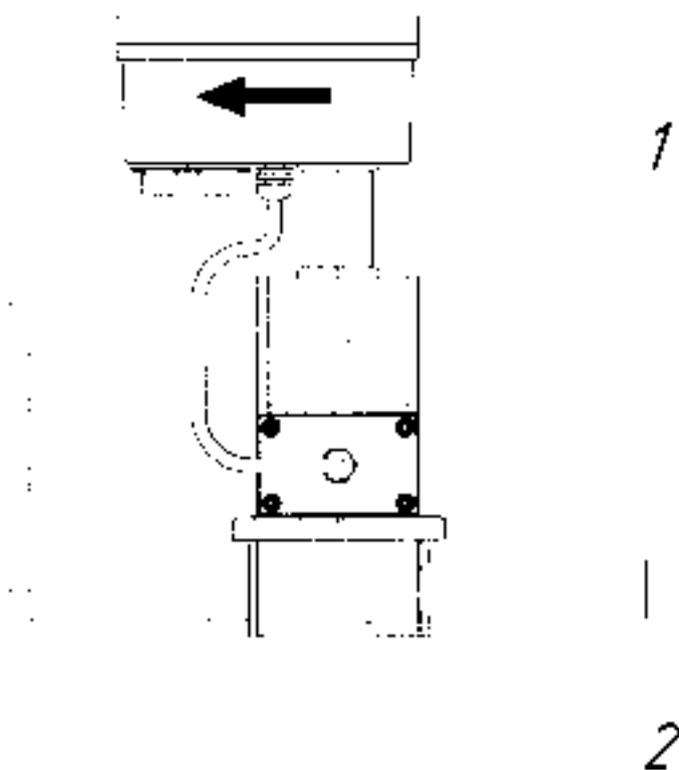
Схема установки ПР через установочный блок на поверочную установку
